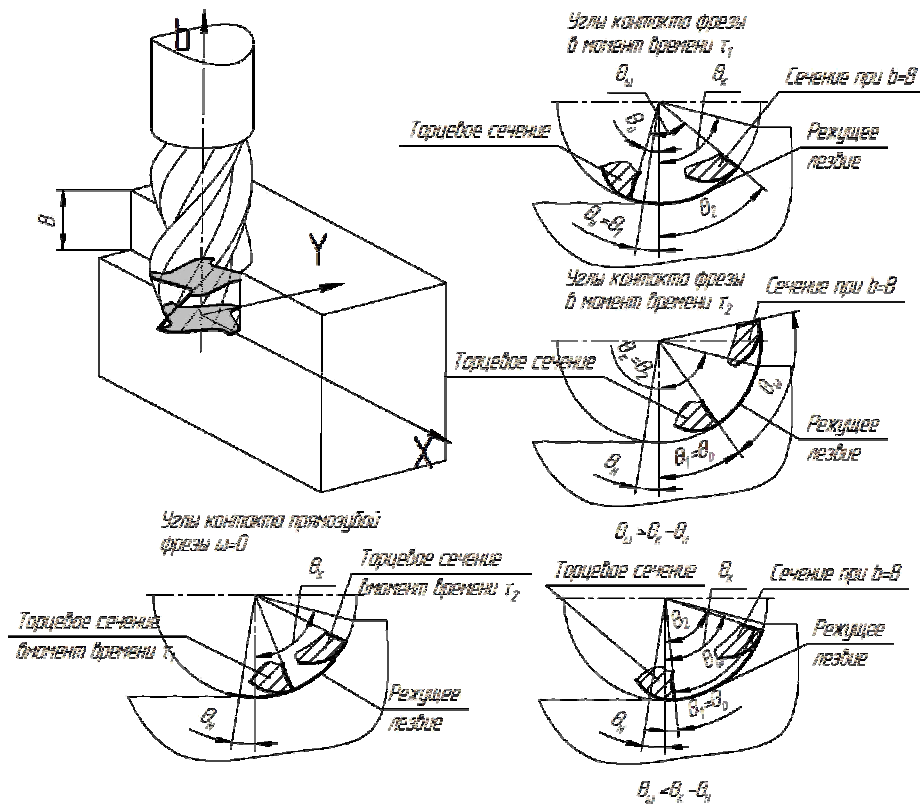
Расчетная схема для определения углов контакта фрезы с заготовкой
